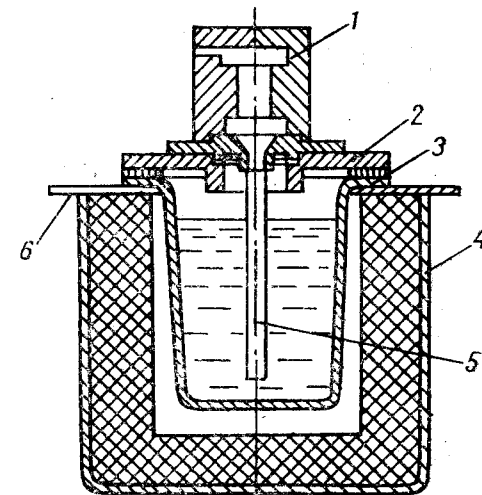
Схема виливання заготовки під низьким тиском:
